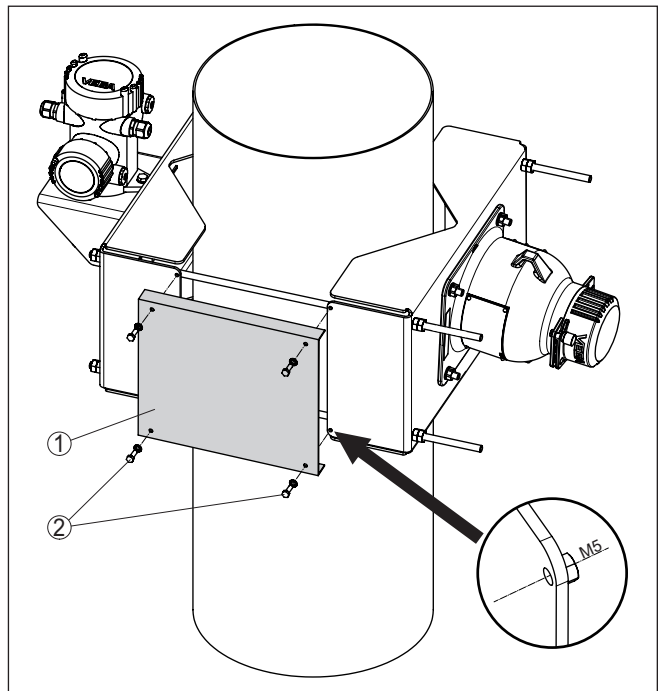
Apposer une grille de protection sur les deux côtés du dispositif de fixation
